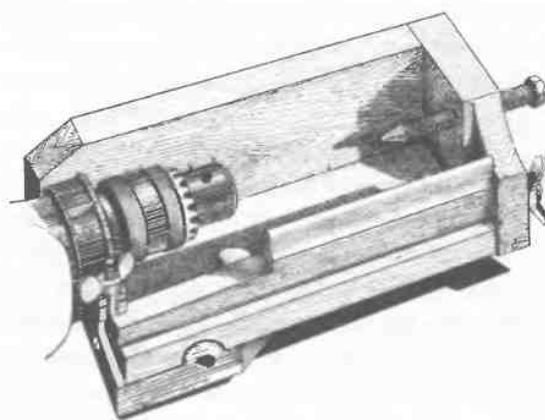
Приспособление, позволяющее использовать электродрель в качестве ручного токарного станка для мелких поделок
